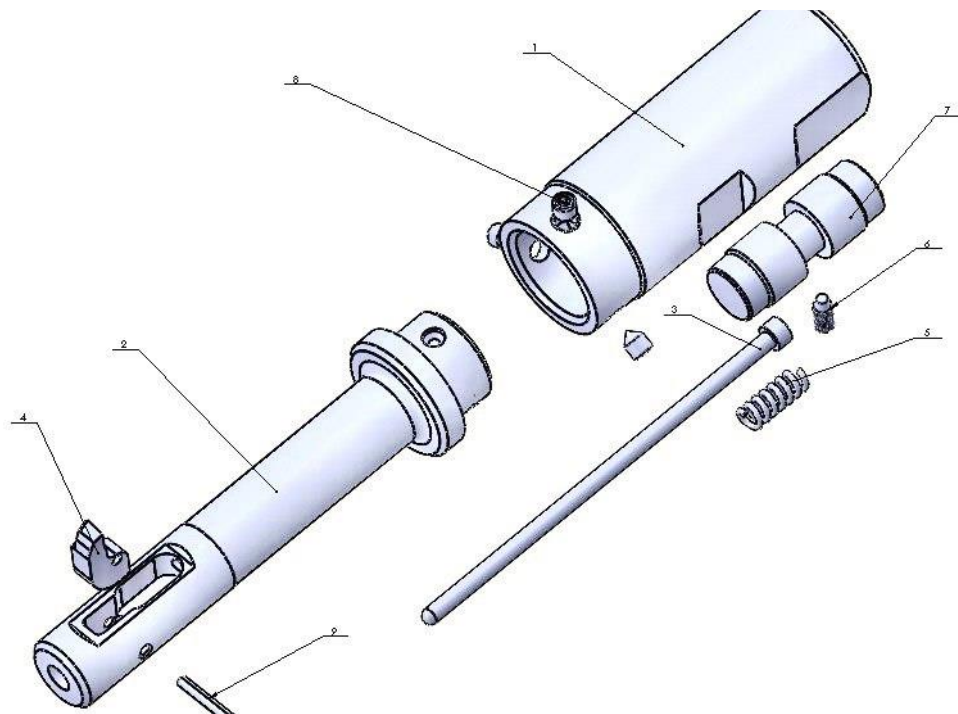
Схема головки розточної збірної для оброблення закритих поверхонь
